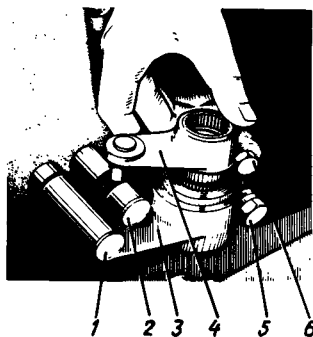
Регулировка привода управления зубчатыми муфтами грузового вала и заднего хода
